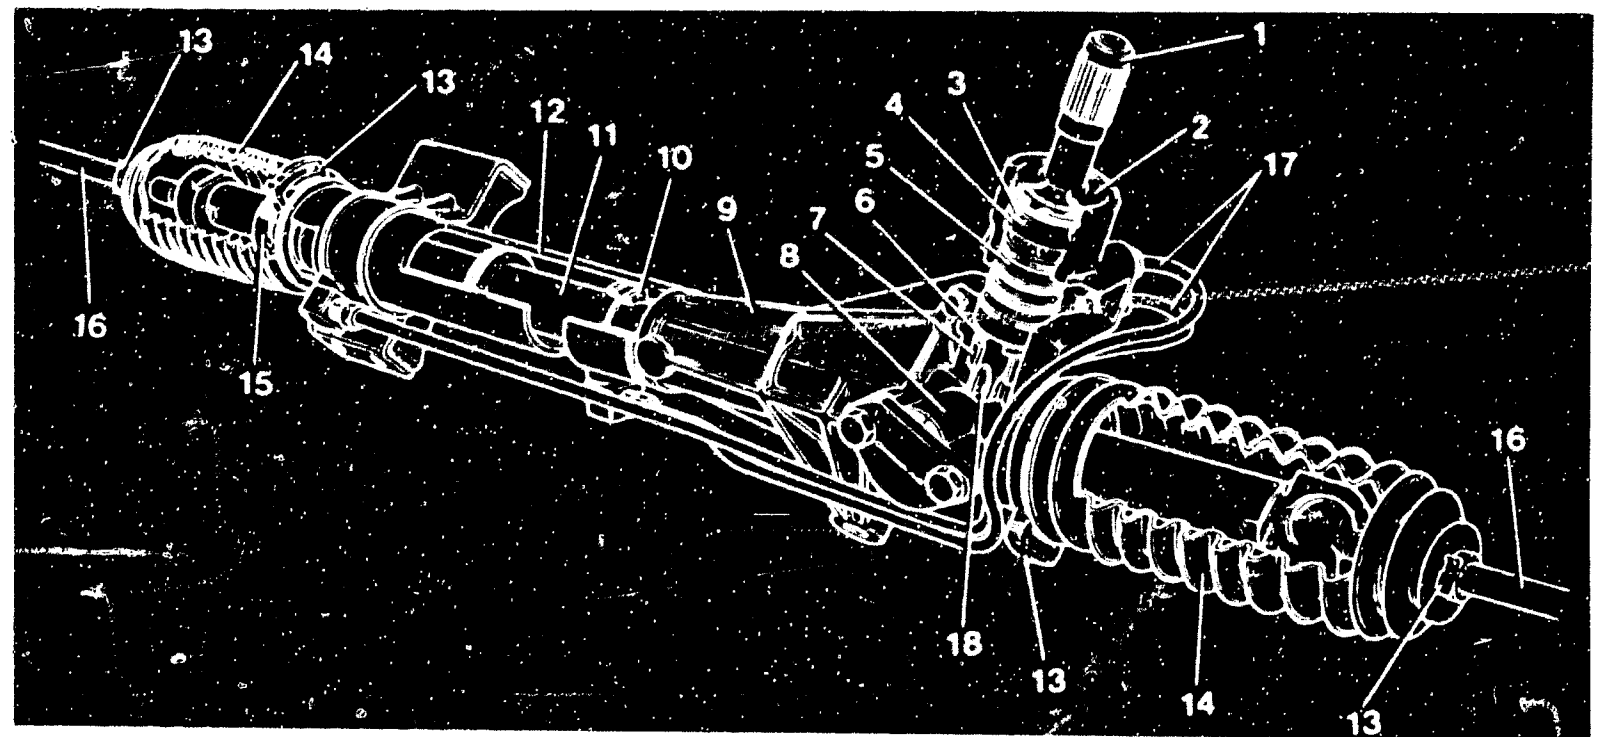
Zahnstangenlenkung mit hydraulischer Unterstützung: 1 Schneckenwelle – 2 Staubkappe – 3 Dichtring – 4 Obere Schneckenrollenlager – 5 Steuerschieber am Schneckenkopf – 6 Dichtring – 7 Gleitlager – 8 Nachstellkolben – 9 Lenkgehäuse – 10 Dichtring – 11 Zahnstange – 12 Zahnstangenrohr – 13 Klammer – 14 Gummibalg – 15 Gleitlager – 16 Lenkschubstange – 17 Ölleitungen – 18 Lenkschnecke.
